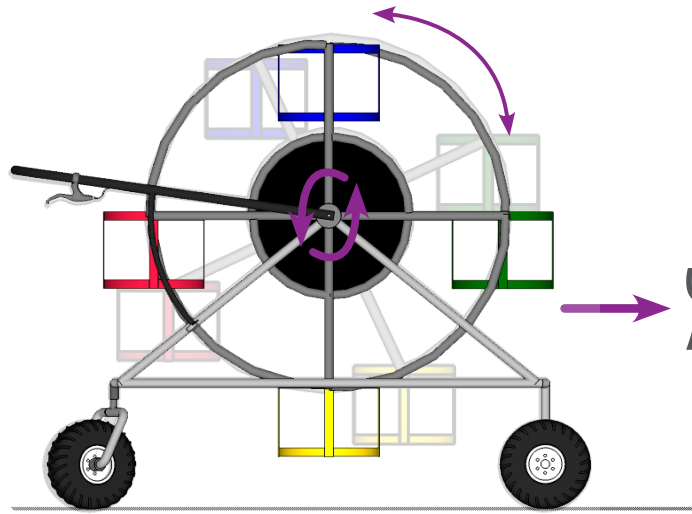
Este eje permiten que giren las canastas en conjunto, gira en ambas direcciones.
